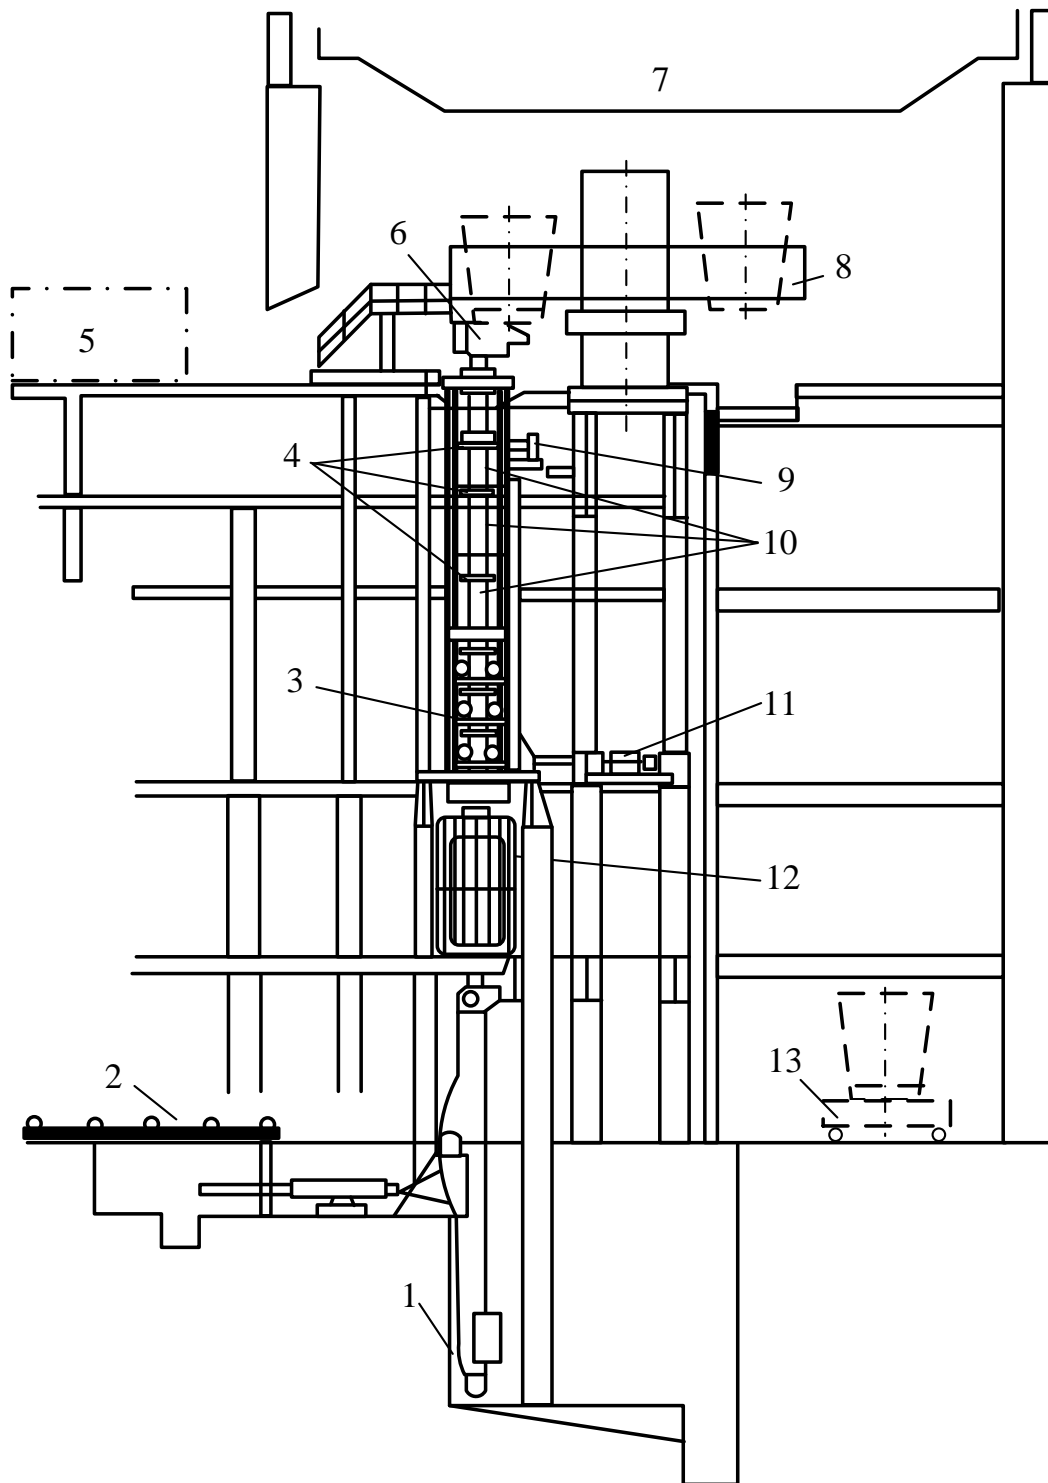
Схема центробежной МНЛЗ: 1 – кантователь; 2 – отводящий рольганг; 3 – тянущая клеть; 4 – направляющие ролики; 5 – пост управления; 6 – промежуточный ковш; 7 – разливочный кран; 8 – поворотный стенд; 9 – механизм качения кристаллизатора; 10 – ЗВО; 11 – привод тянущей клетки; 12 – пила горячей резки; 13 – стелевозная тележка
